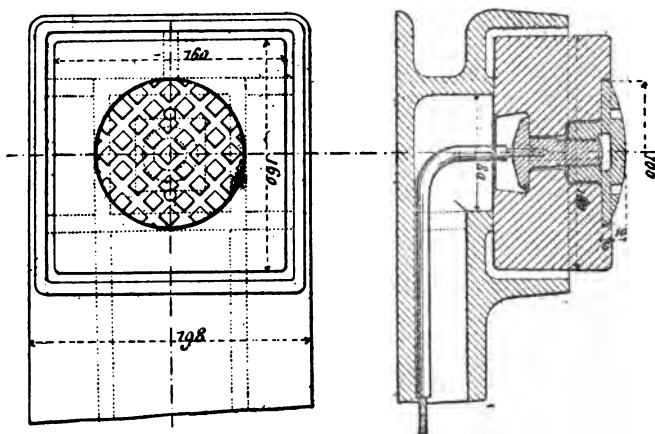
et 96. — Coupe et plan du bouton de contact Westinghouse.
